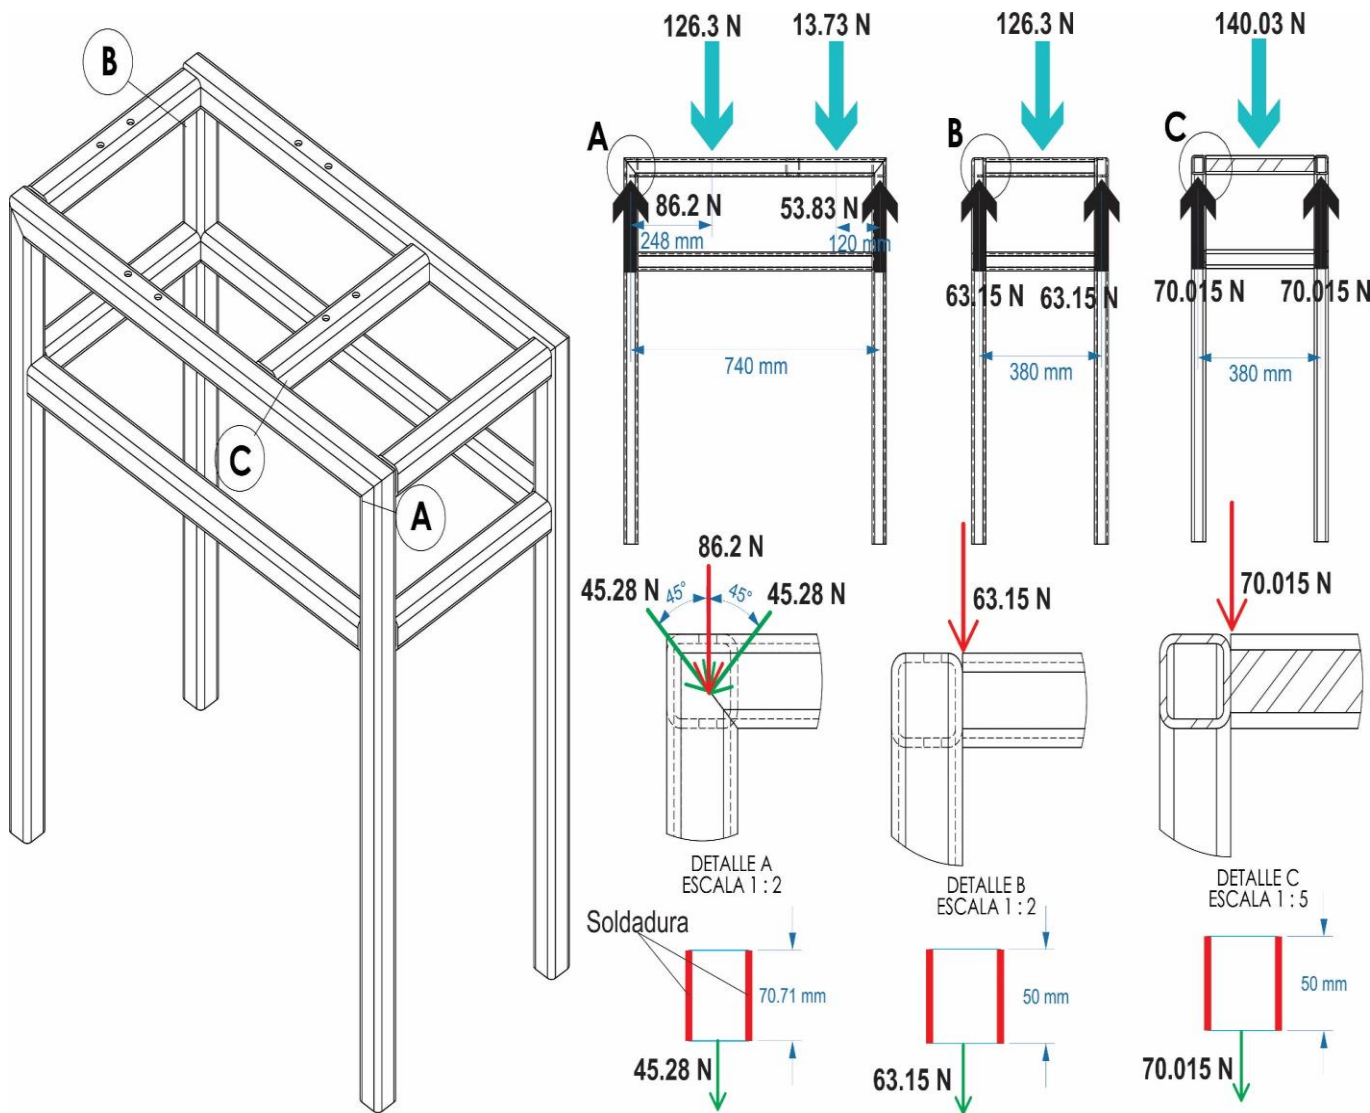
Zonas de análisis de soldadura, Detalle A: DCL y Cargas de la viga principal, Detalle B: DCL y Cargas de la viga Lateral, Detalle C: DCL y Cargas de la viga media
